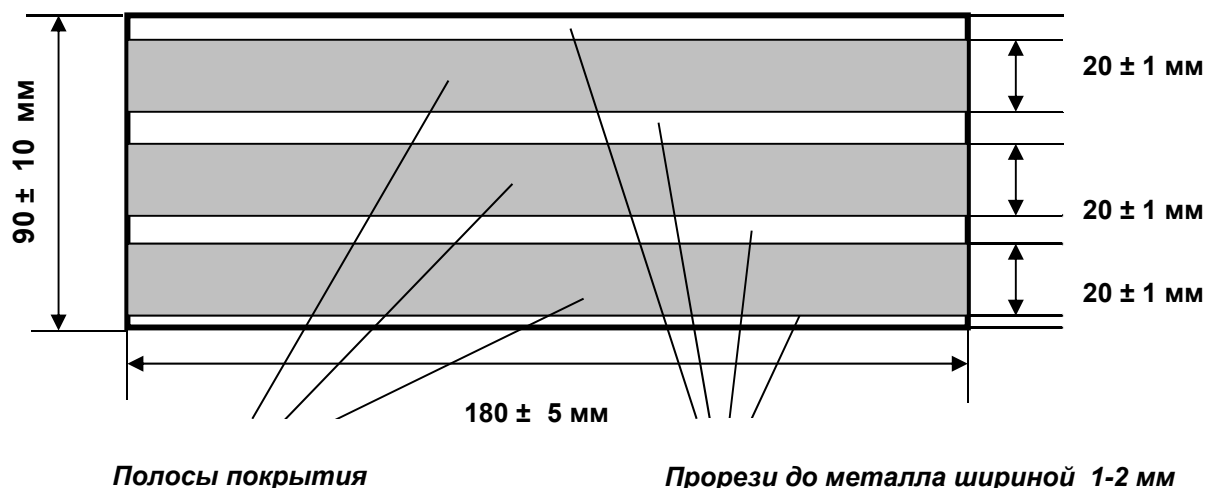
Эскиз образца для испытаний на адгезию.
